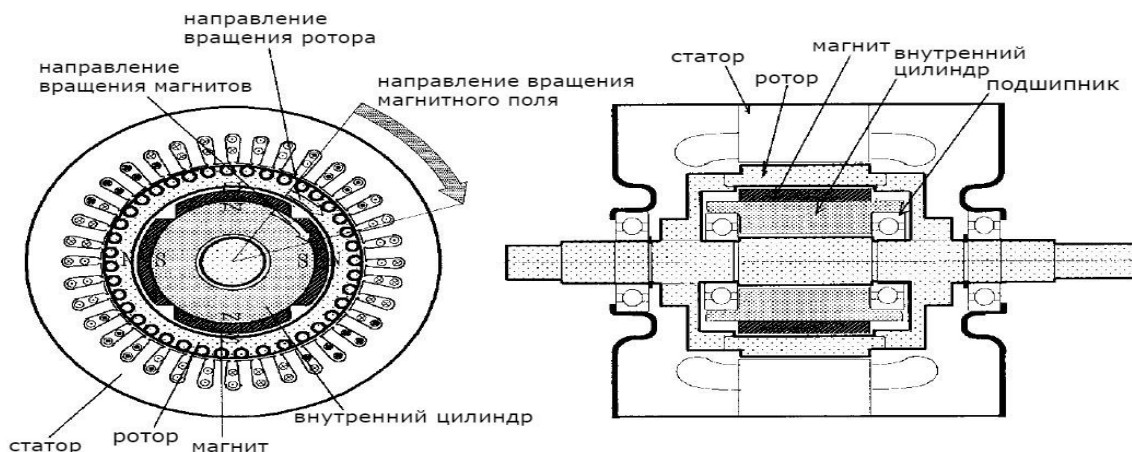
Асинхронный двигатель со свободно вращающимися магнитами внутри ротора
